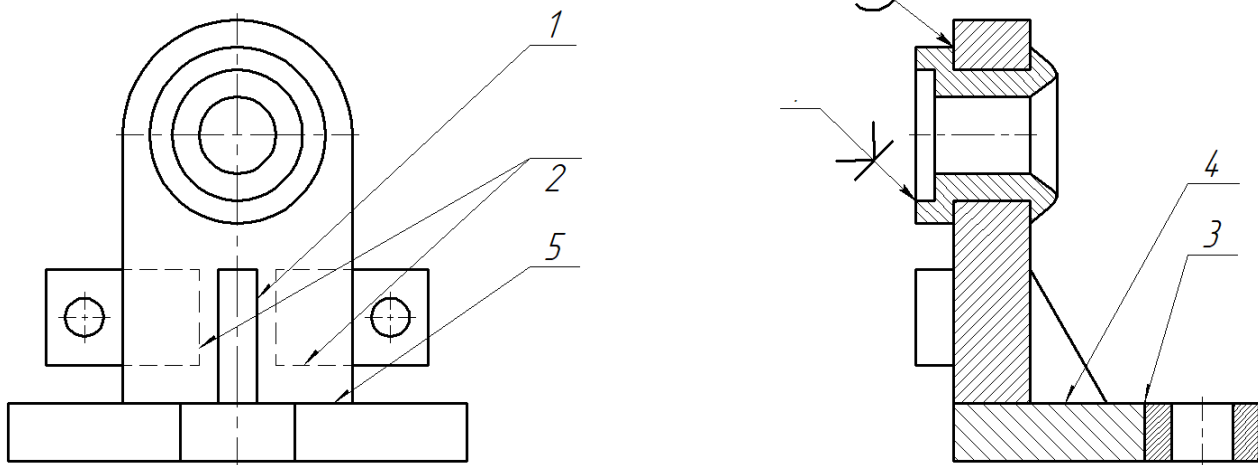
Номера обозначений сварных швов по заданию
